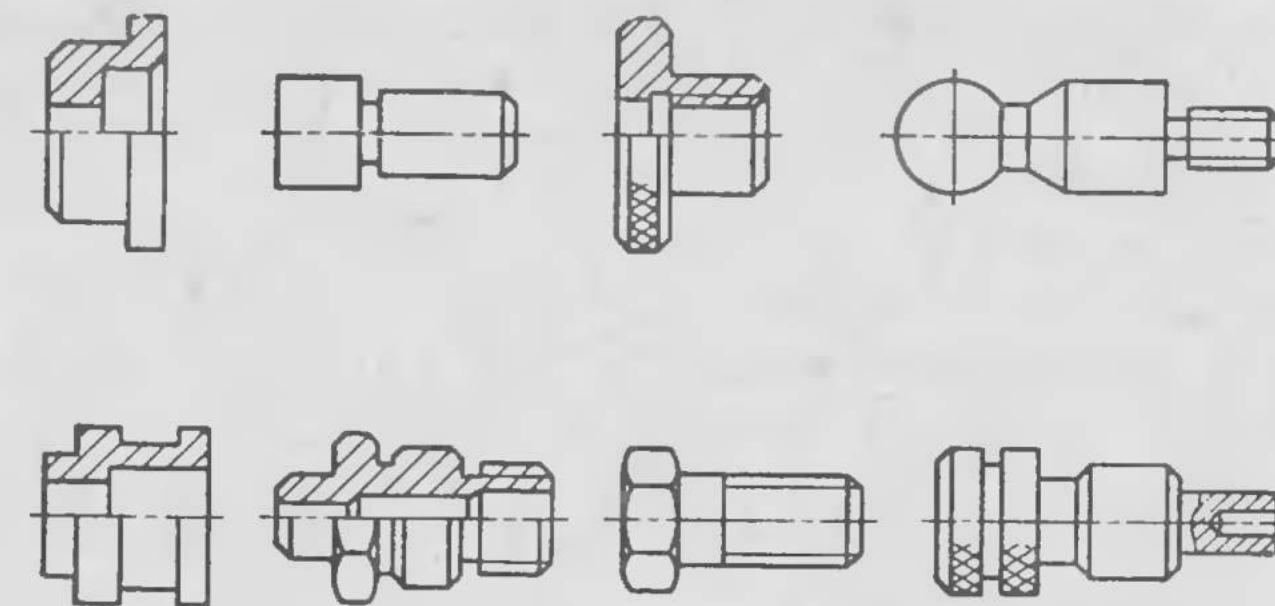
Типовые детали, обрабатываемые на токарно-револьверных автоматах
